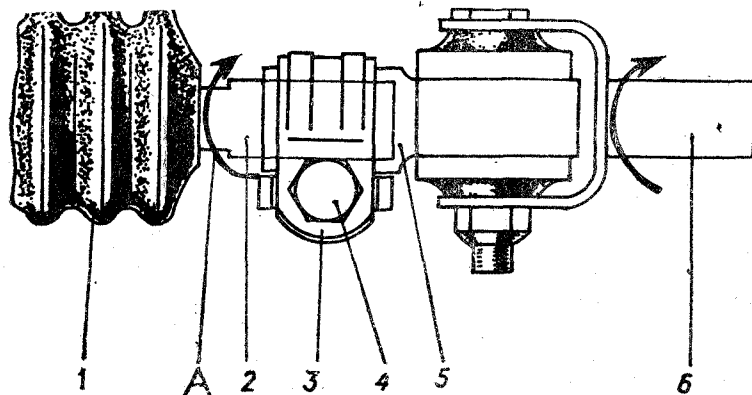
Регулировка привода управления коробкой передач (вид снизу):
